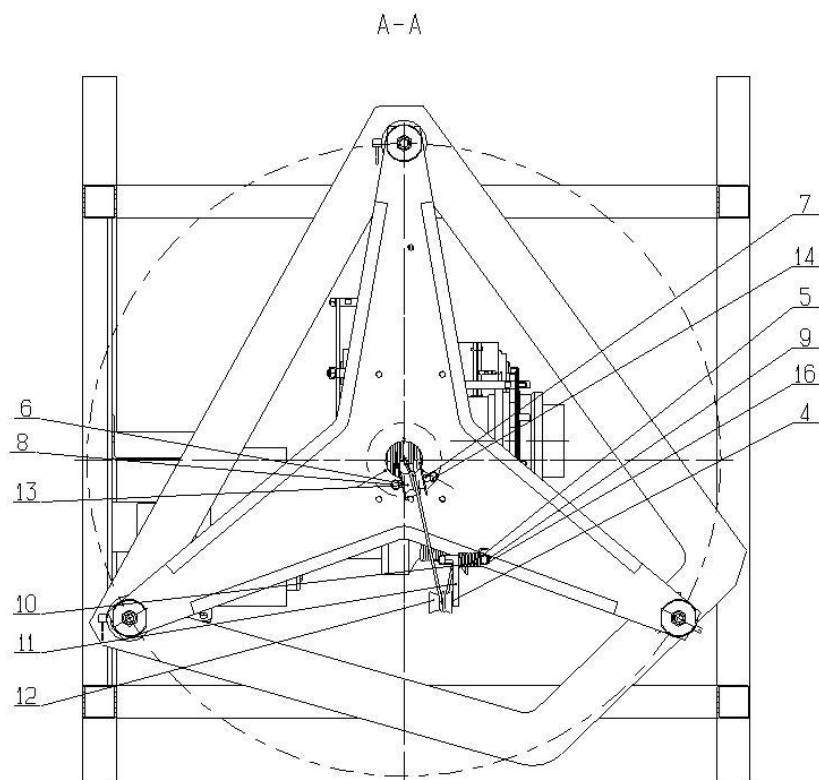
Общая компоновка лабораторного стенда (разрез А – А)
